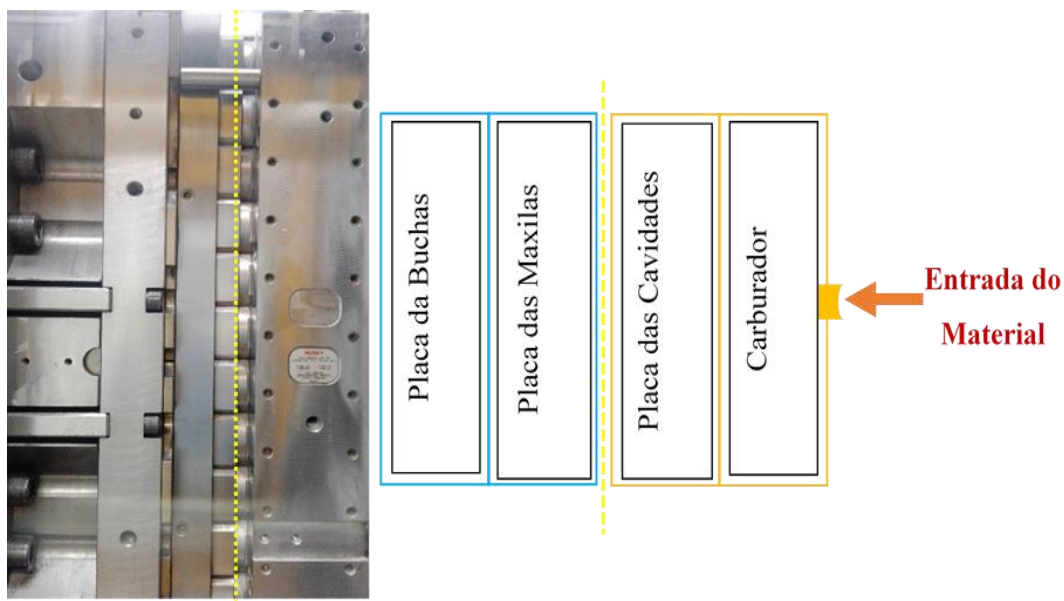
Constituição base de um molde de injeção de pré-formas
